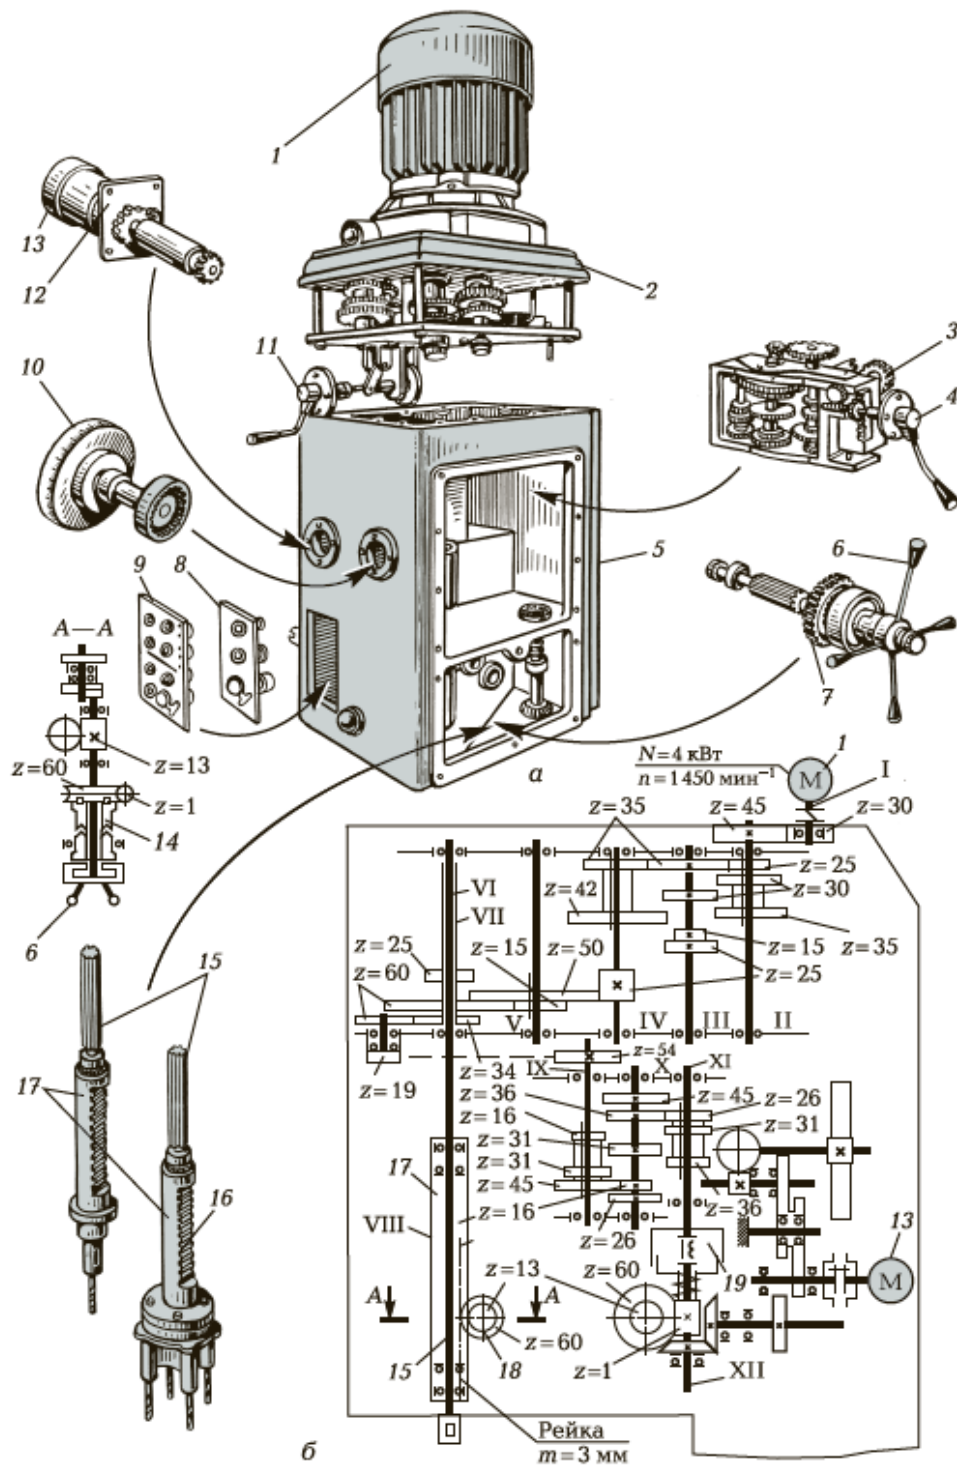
Сверлильная головка (а) и кинематическая схема (б) вертикально-сверлильного станка:
